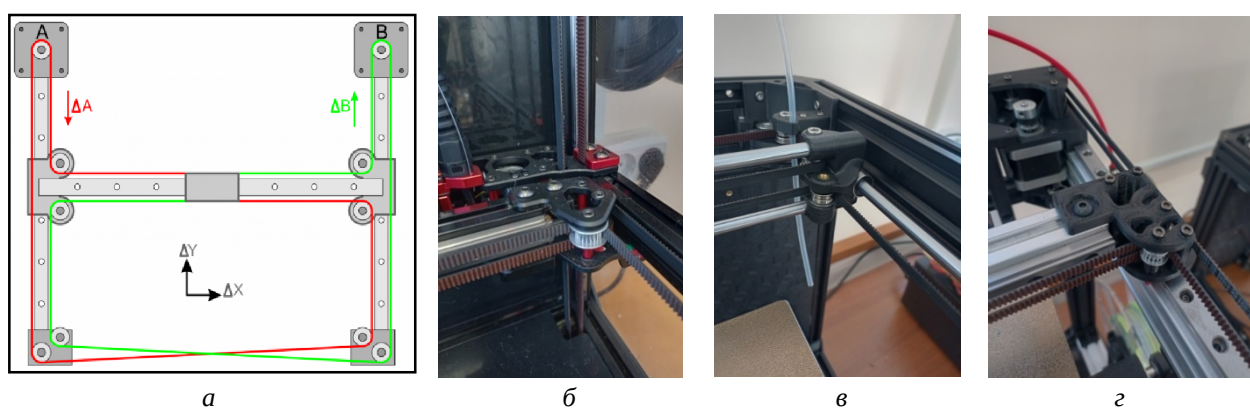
Схема портала с кинематикой CoreXY (a) и способы крепления портала:
